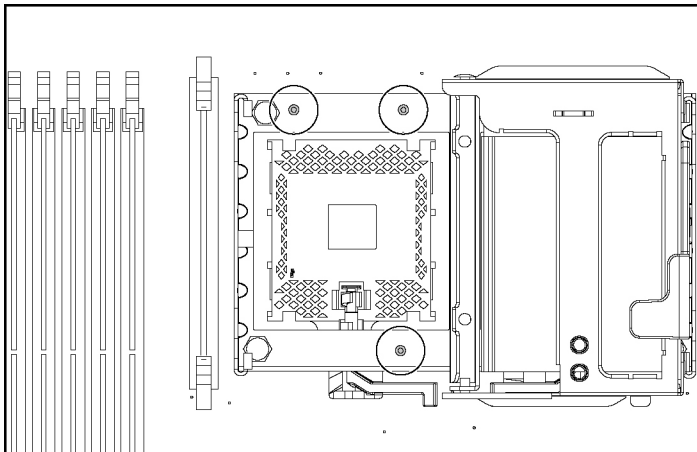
Ausrichten der Prozessorbaugruppe für die Installation
